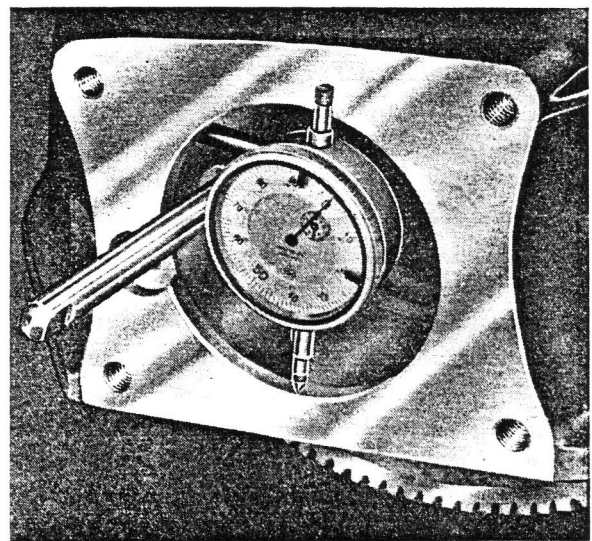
Messen des Schwungradgehäuses mit Messuhr
